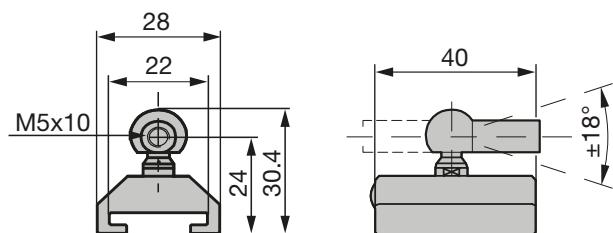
Dimensions de montage du capteur de position BTL5-F-2814-1S
